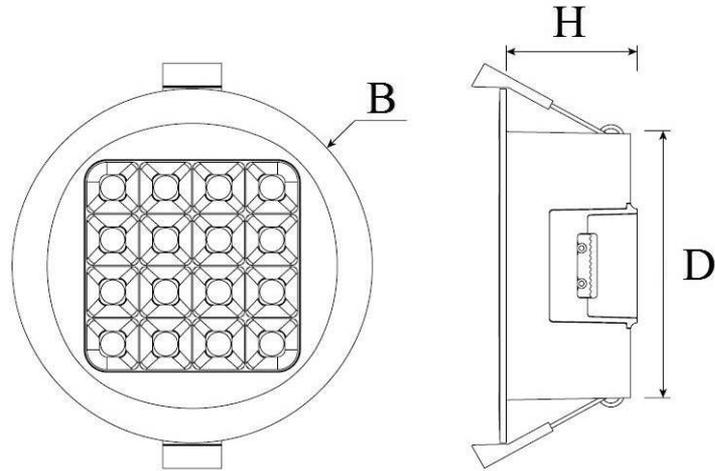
Внешний вид светильника ДВО20 DLD
